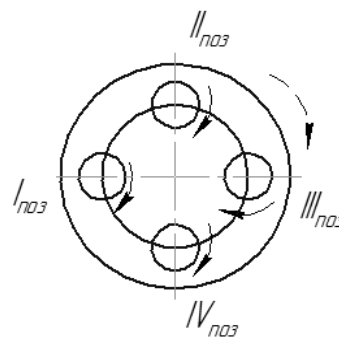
Позиції, які по чергово займає заготовка при обробці на 4-шпиндельному токарному автоматі
